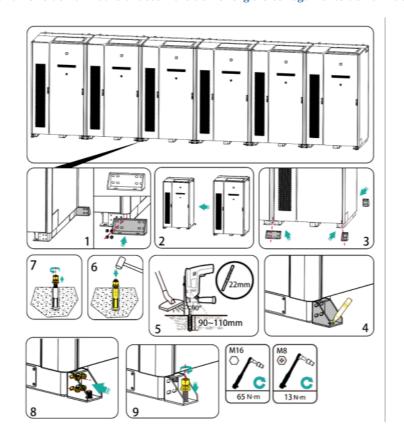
Schema di installazione del collegamento degli armadi di accumulo dell'energia
